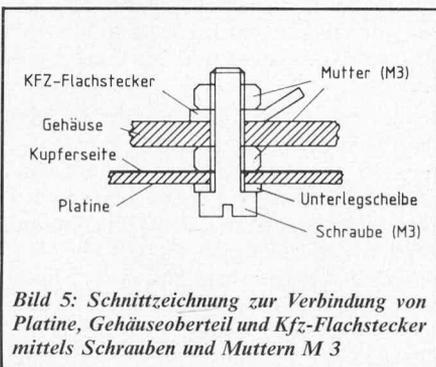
Schnittzeichnung zur Verbindung von Platine, Gehäuseoberteil und Kfz-Flachstecker mittels Schrauben und Muttern M 3
